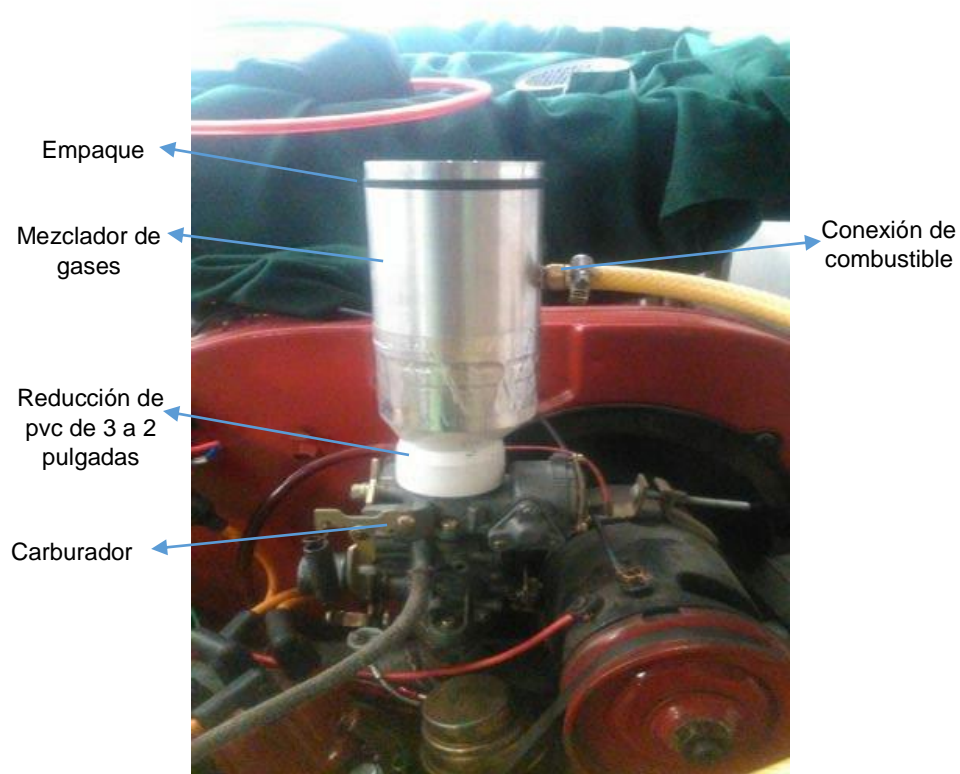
Ensamble del mezclador de gases en el motor del Volkswagen 1600 cm³.
